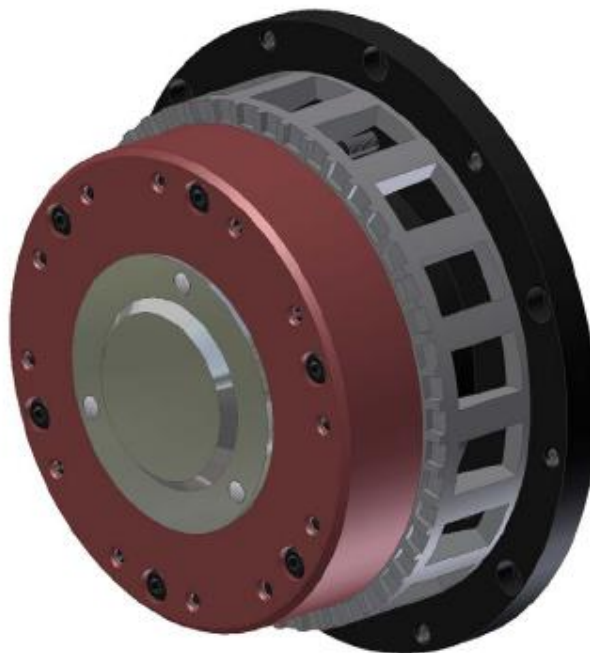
Механический тормоз юнибуса Ю-324П
